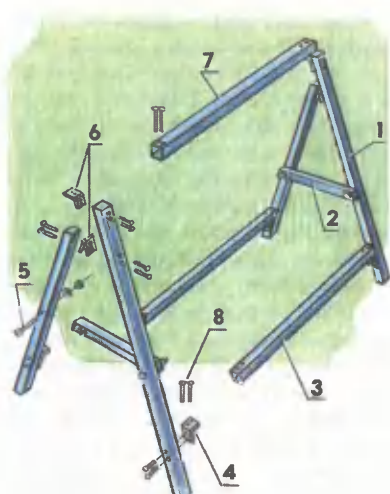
Схема сборки стоек-ножек: 1 — стойки; 2 — заселка; 3 — глухая стяжка на заклепках; 4 — дюралюминиевый уголок; 5 — болт с шайбой и гайкой; 6 — петли на заклепках; 7 — несущая перекладина; 8 — заклепки.
